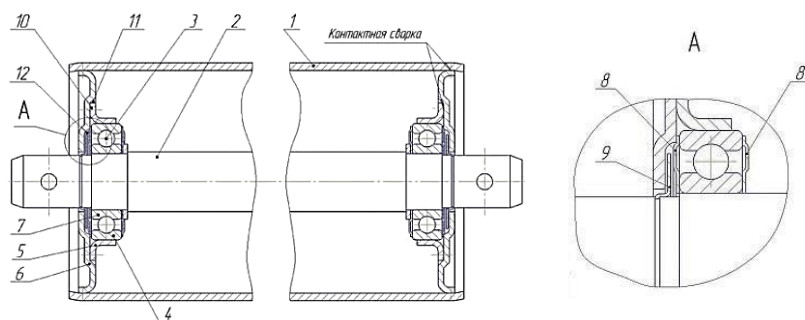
Конструкция разработанного ролика ленточного конвейера
